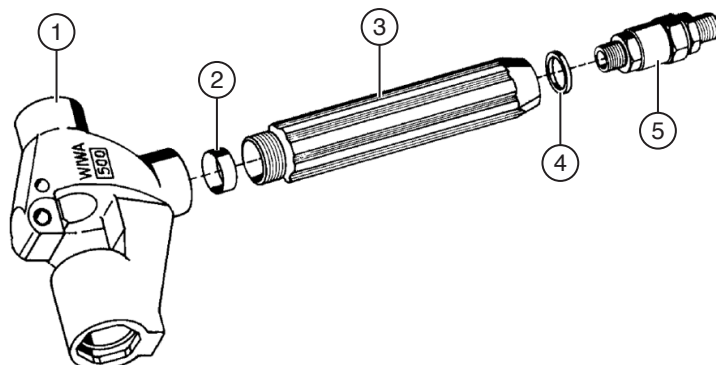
Dichtungen des Pistolengriffs ausbauen (WIWA 500 und WIWA 500 D)
